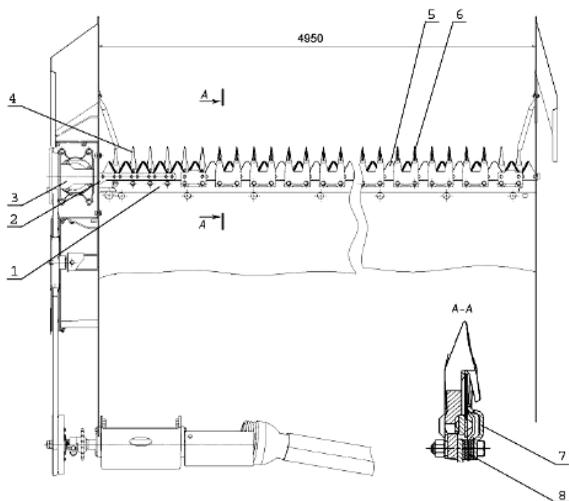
Режущий аппарат: 1 – пальцевой брус; 2 – пятка ножа; 3 – кривошип редуктора; 4 – палец; 5 – сегмент; 6 – нож; 7 – прижим; 8 – прокладки
